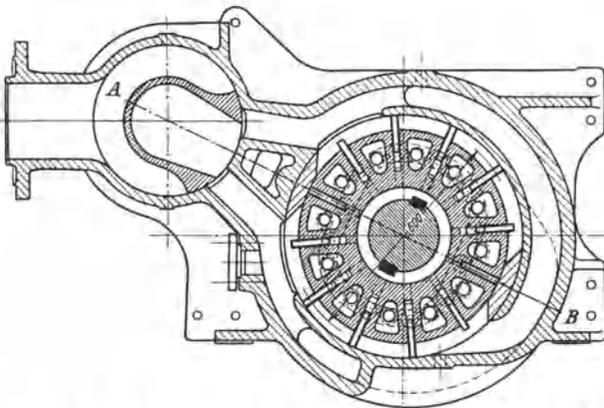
a. Kapselmotor des Lenz-Getriebes. (Dieselmaschinen II. S. 72.)
